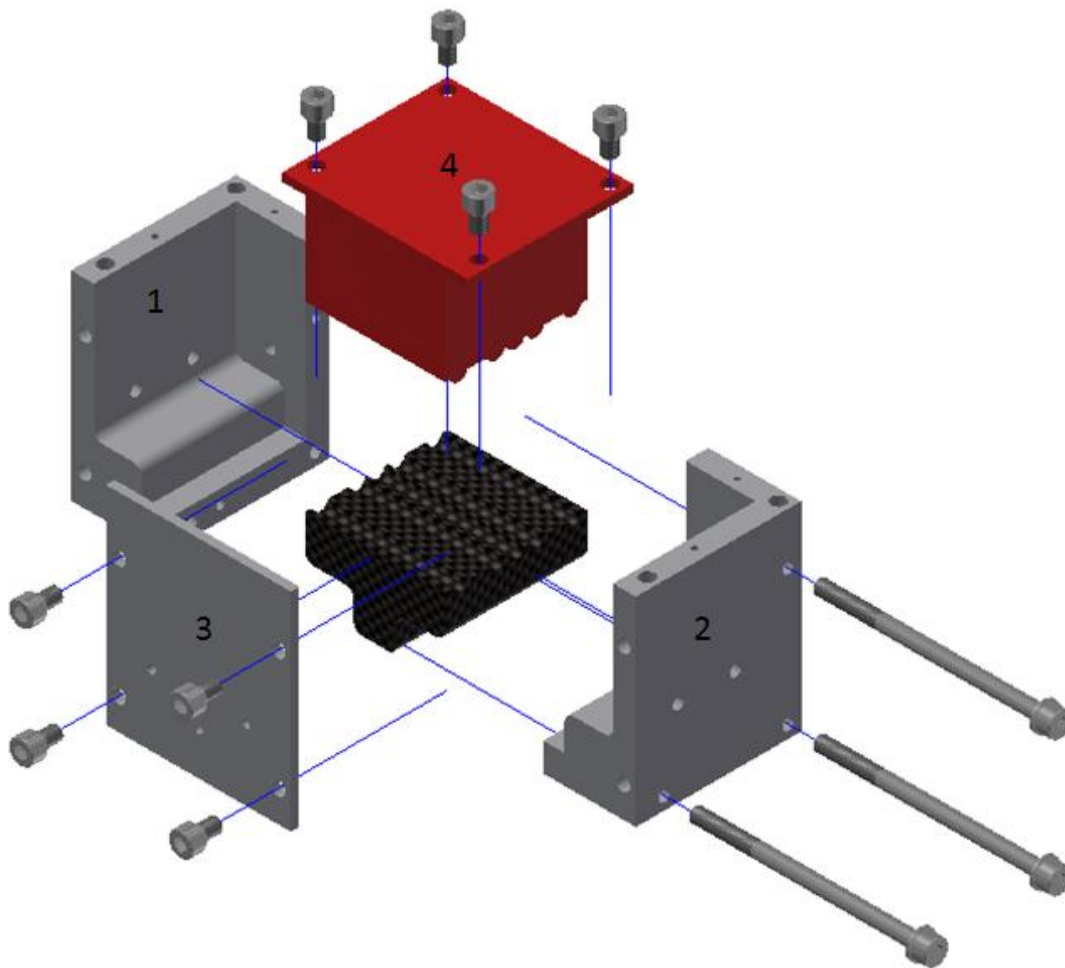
MOLDE PARA FABRICACION DE PIEZA EN FORMA DE T EXPLOSIONADO.
